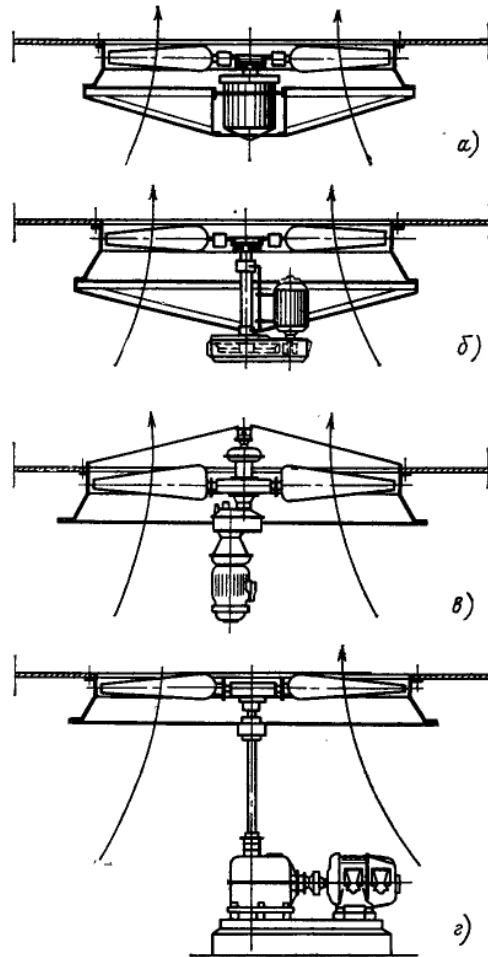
Привід вентилятора: а) прямий привід, б) клиноремінна передача, в) підвісний привід з редуктором, г) виносний привід з редуктором.
